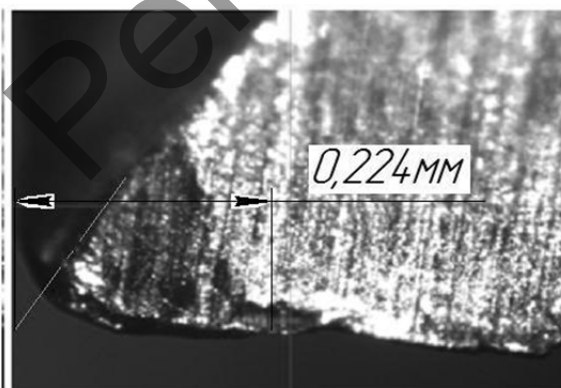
Вид концевой фрезой со стороны вспомогательного лезвия фрезы
